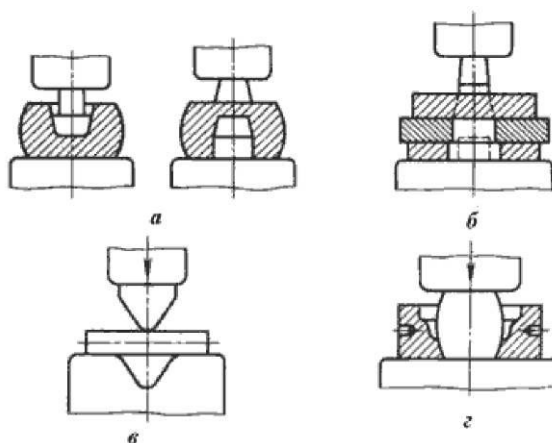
Схемы прошивки (а, б), гибки (в), штамповки в подкладных штампах (г)
